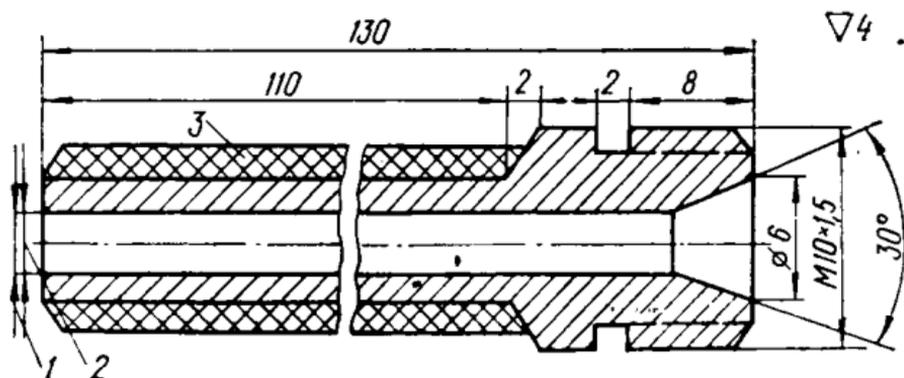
Удлиненный мундштук для полуавтоматической ванно-шлаковой сварки стыков рельсов:
